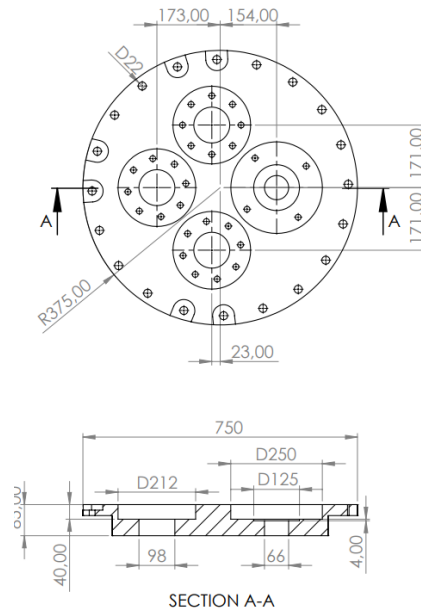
Planta y sección de la tapa acotada. Fuente propia.
